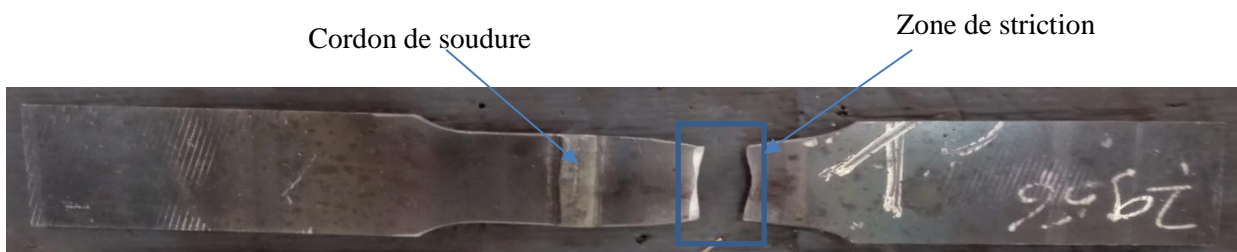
éprouvette avec cordon de soudure après rupture
